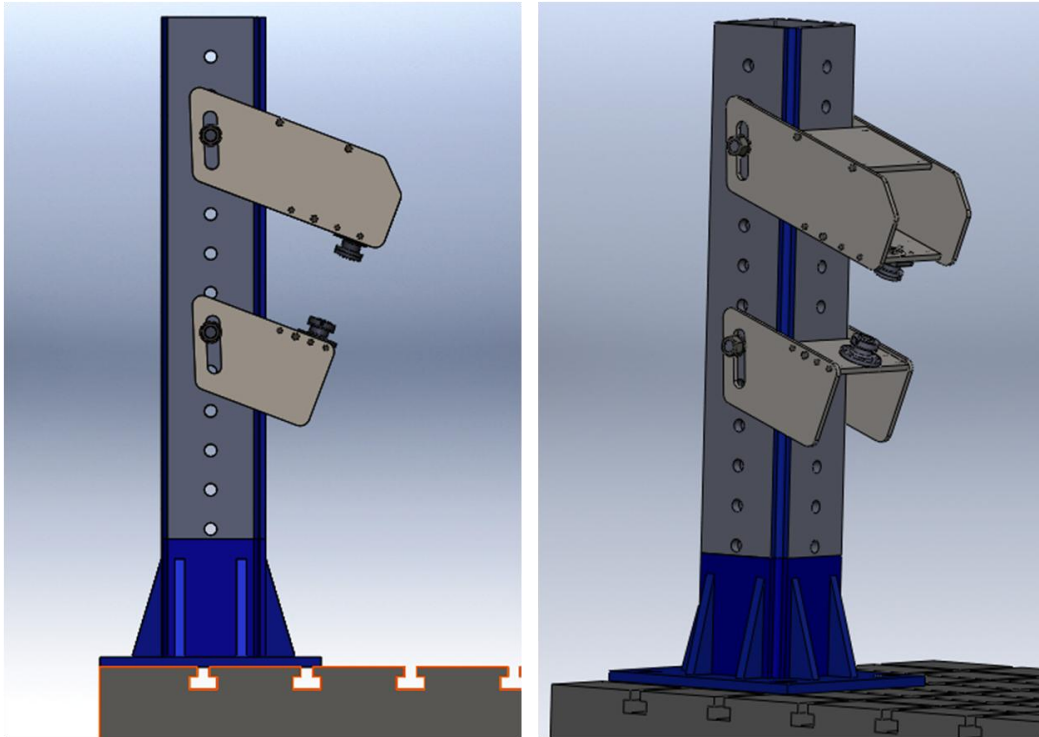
Assieme colonna e piastre di afferraggio canotto di sterzo
